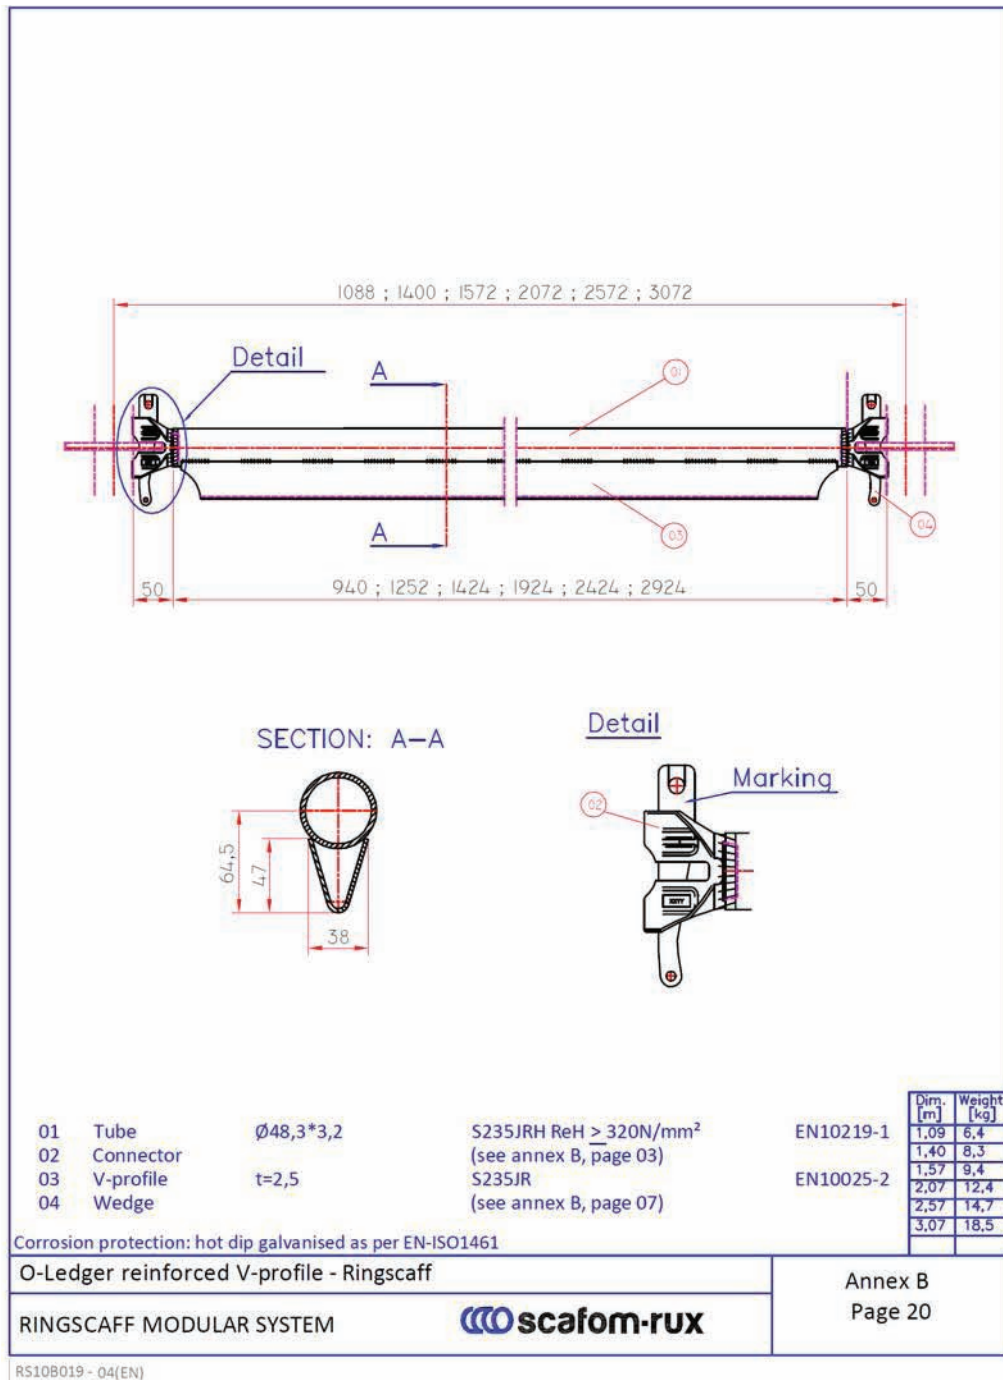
Travessa com secção tubular reforçada com perfil em V
